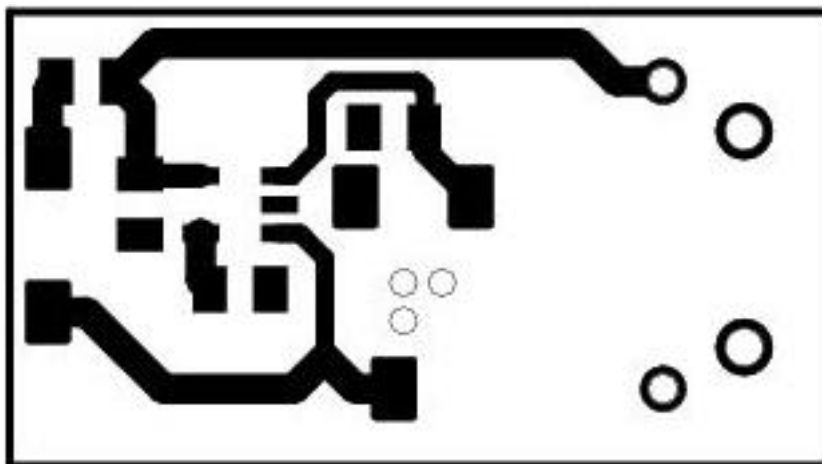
Strana spojů SugarCube - vrstva BOTTOM, měřítko 4:1
